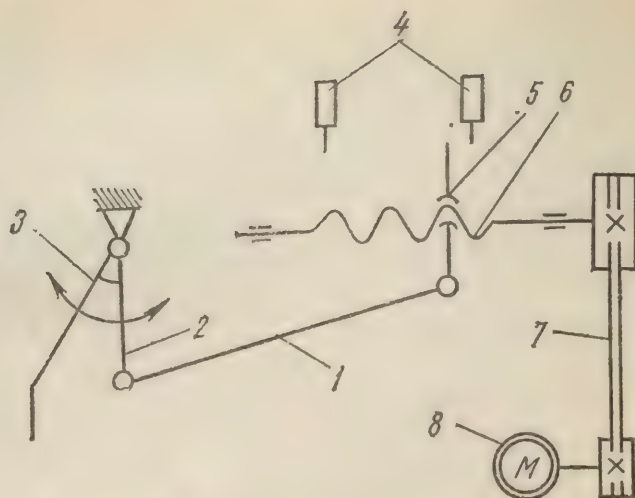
Схема привода для открытия шибер загрузочного ковша
